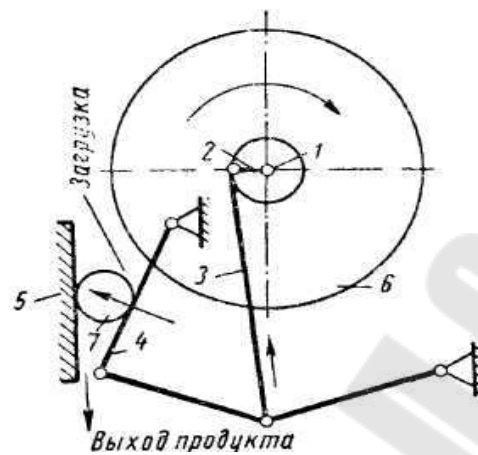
Кинематическая схема щековой дробилки: 1- вал; 2- кривошип; 3- шатун; 4- качающаяся щека; 5- неподвижная щека; 6- маховик; 7- кусок материала
